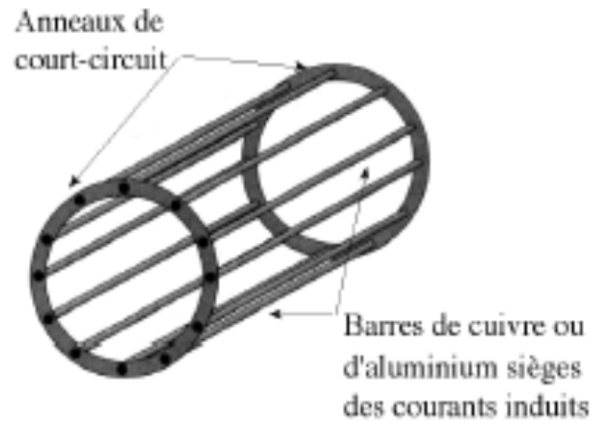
vue de la cage d'écureuil du rotor de la machine asynchrone seul
